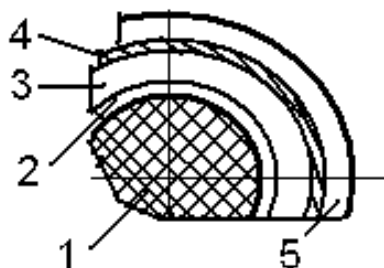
Схематический разрез формного цилиндра глубокой печати
